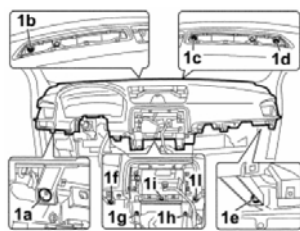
Collegamenti per il fissaggio di una plancia all'interno della Fiat Croma 2006
